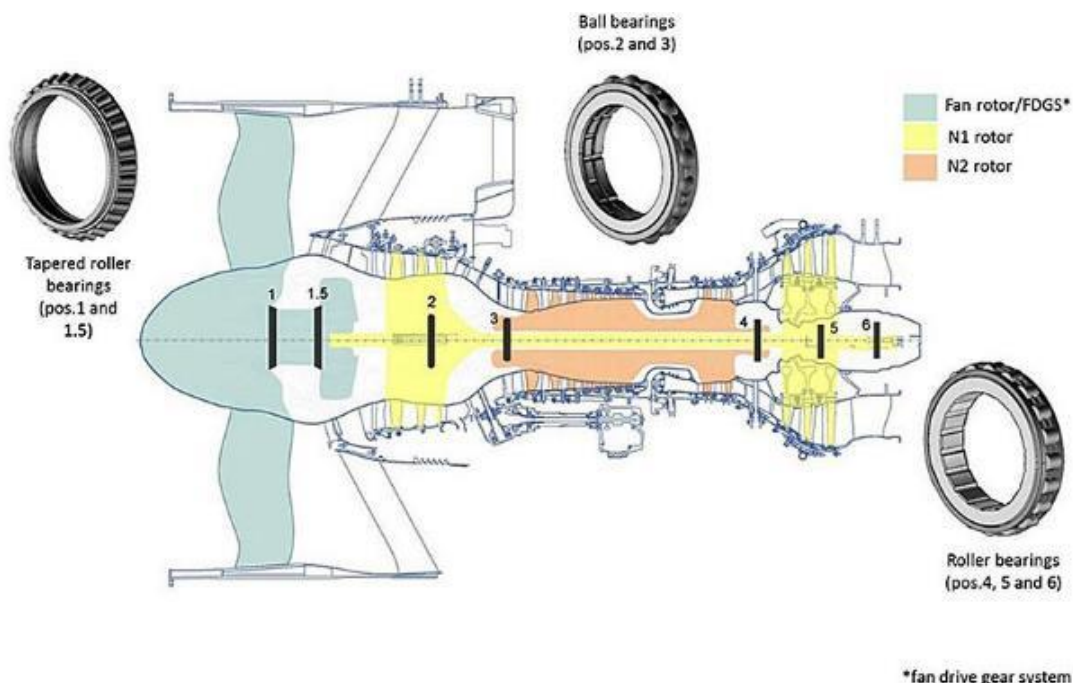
Vue de coupe d'un moteur PW1500 de Pratt & Whitney illustrant la position des roulements. (Bombardier Inc, 2014)
